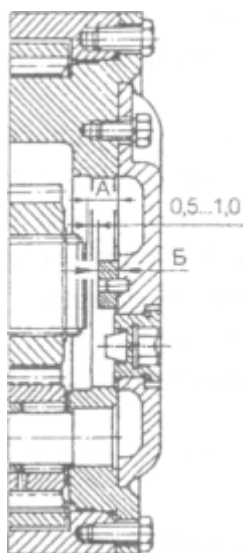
Регулировка зазора между упором крышки водила и полуосью.
